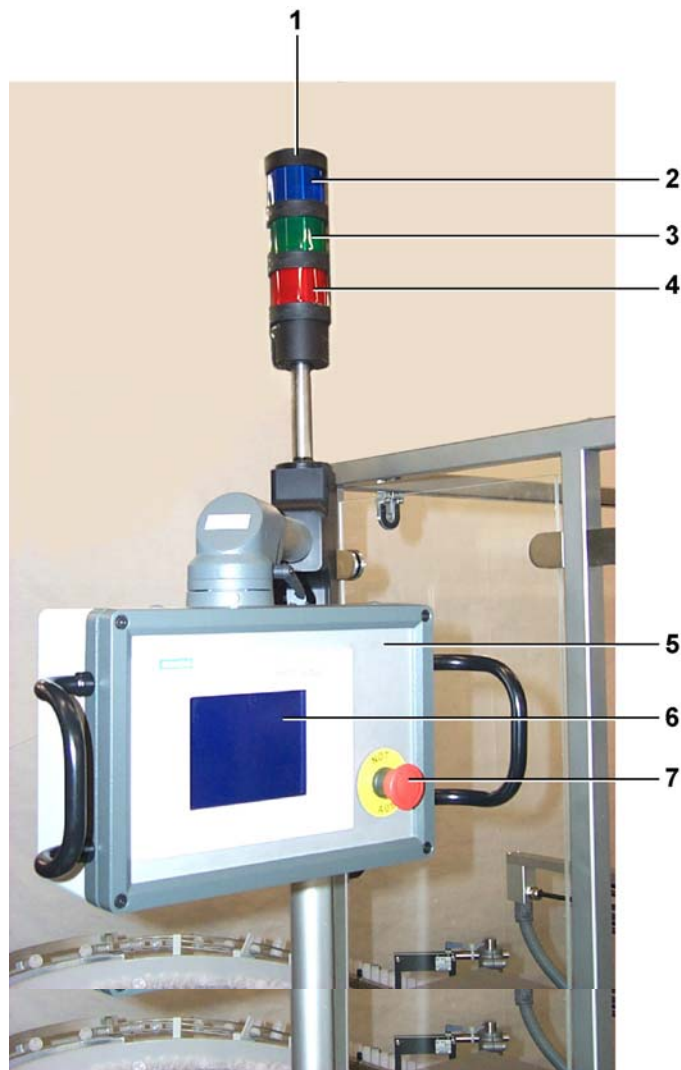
14 Frontansicht Maschine 2 – Module
